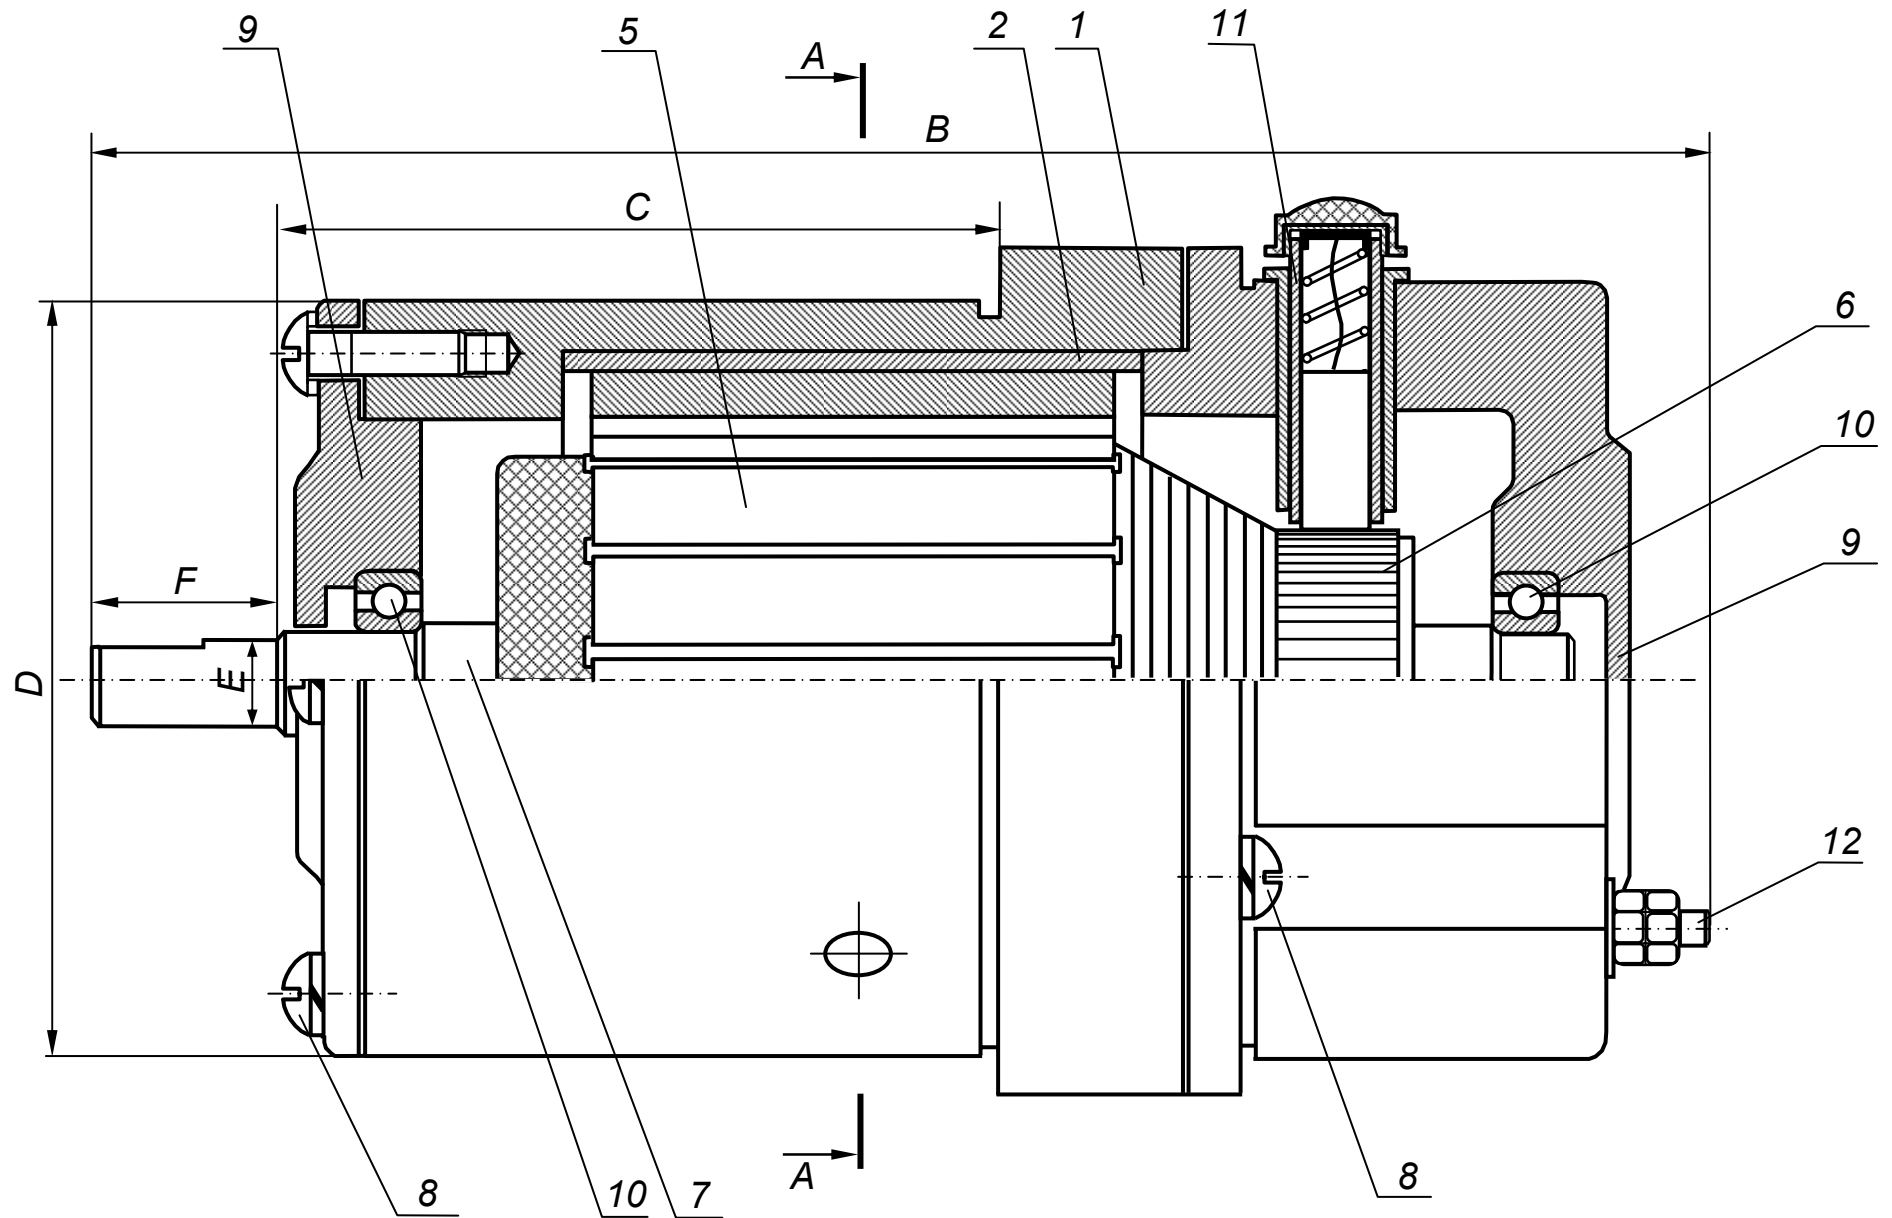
Общий вид двигателя постоянного тока (продольный разрез)
